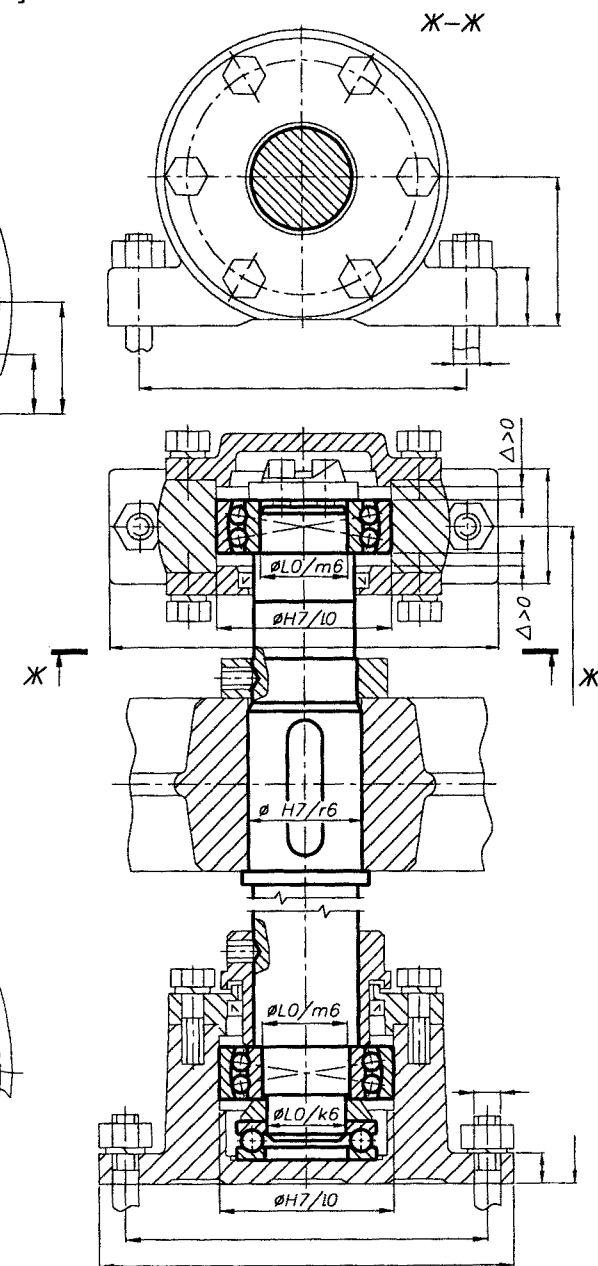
Подшипниковые узлы вертикального приводного вала
